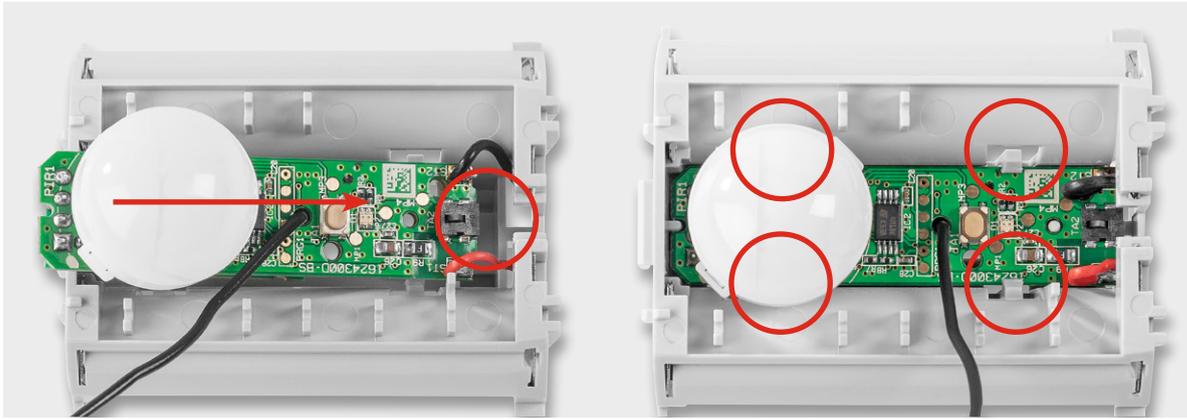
Die Platine ist in Pfeilrichtung (linkes Bild) in das Gehäuse einzulegen, sodass der Sabotagekontakt sauber in die zugehörige Gehäuseöffnung fasst und die Platine in die vier Gehäuserasten (rechtes Bild) einrastet.
